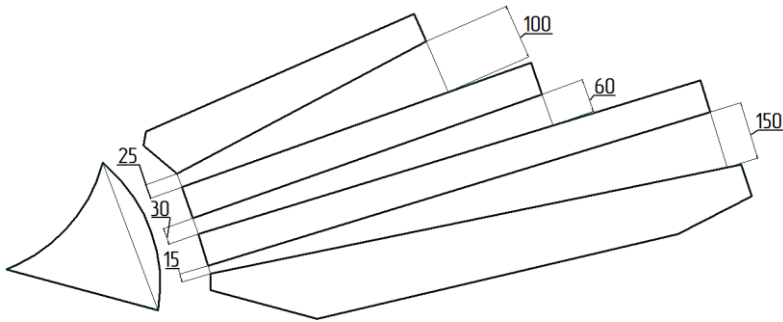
Компоновочная схема пластинчатого корпуса плуга
